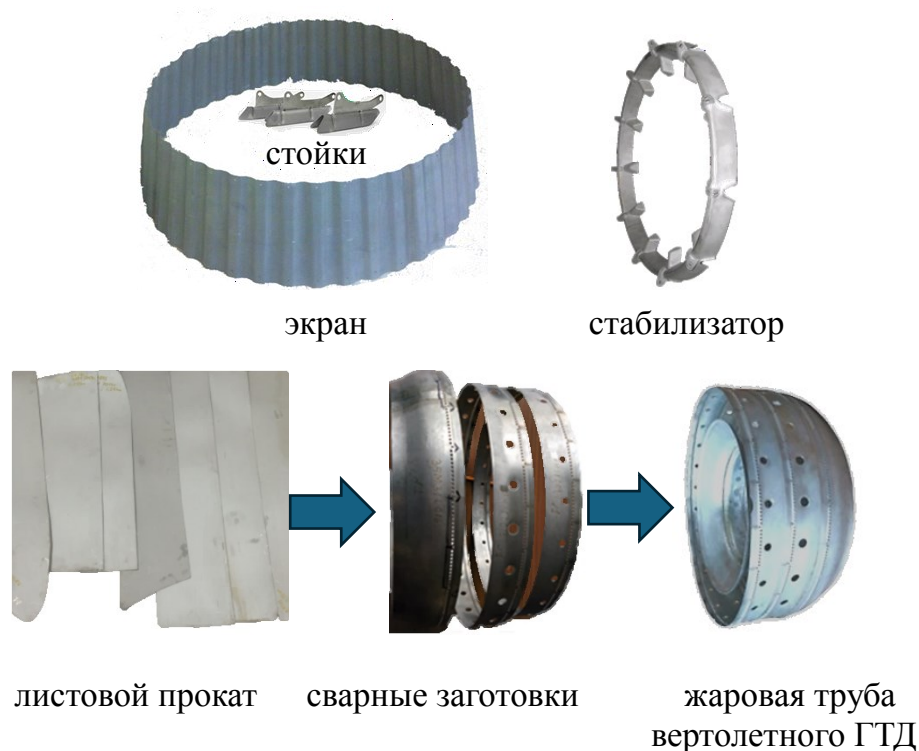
Детали и узлы, изготовленные из сплава ВЖ171
